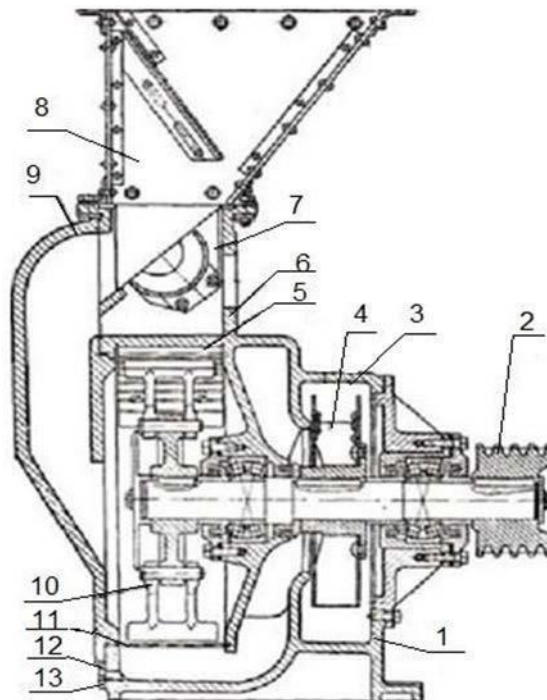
Молоткова дробарка ДДК: 1 – корпус; 2 – шків; 3 – камера для вентиляторного колеса; 4 – вентиляторне колесо; 5 – нерухоме деко; 6 – коробка для магніта; 7 – магніти; 8 – бункер; 9 – кришка; 10 – ротор; 11 – сито; 12 – планка; 13 – щілина для подачі повітря.
